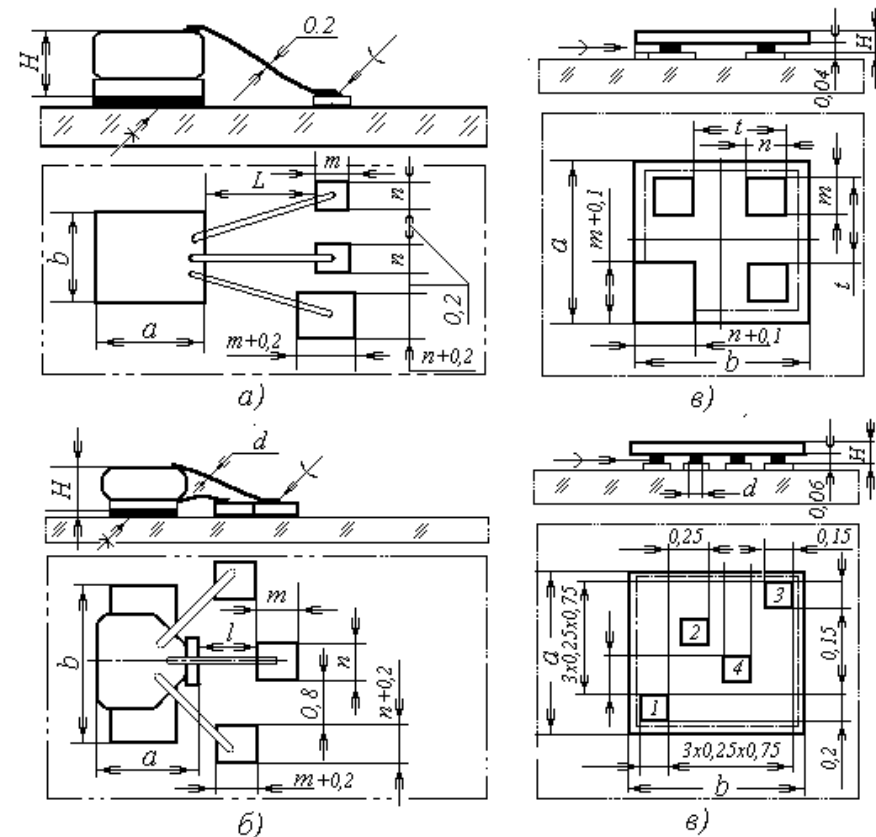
Способы установки , габаритные и присоединительные размеры транзисторов
